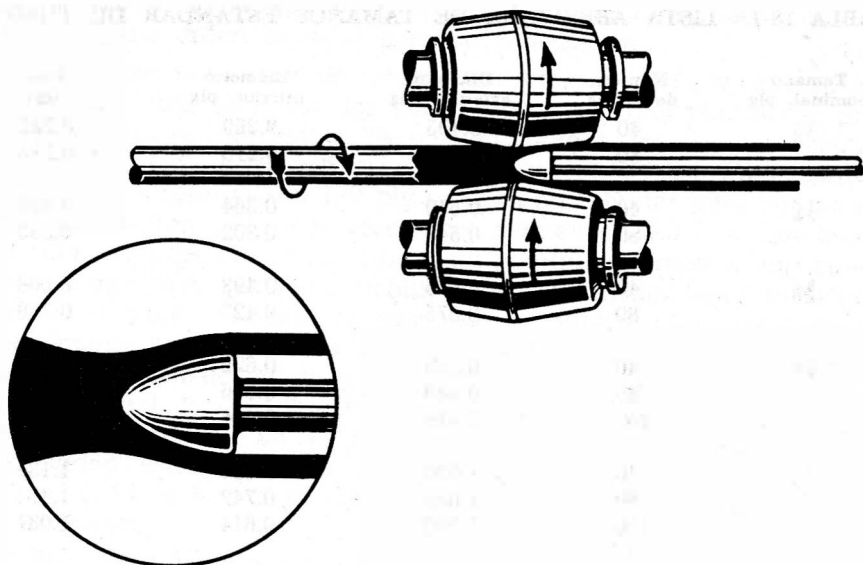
Horadación de un lingote cilíndrico para fabricación de tubo sin costura. (Seamless Steel Institute.)
